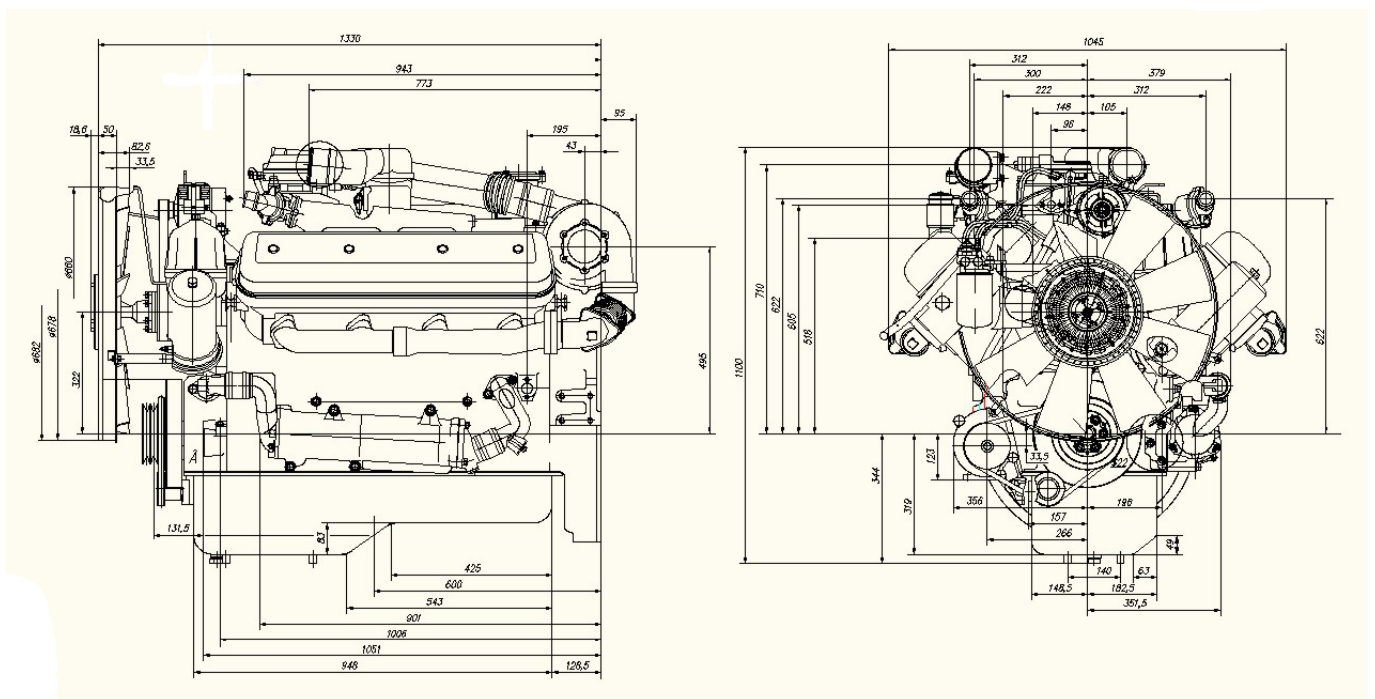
Габаритные размеры (в мм) двигателя ЯМЗ-6585
